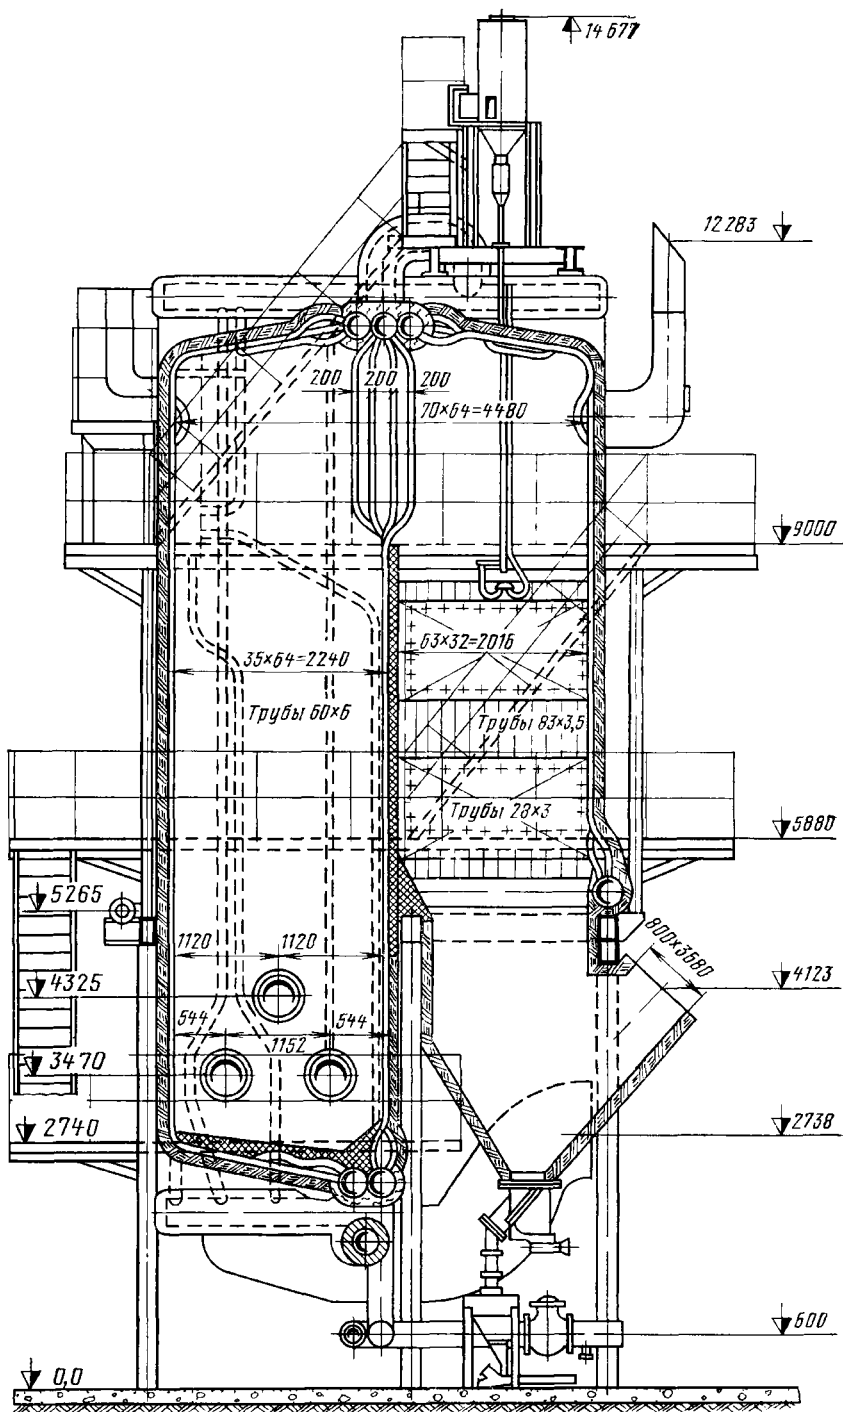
Котлоагрегат ПТВМ-30М.
